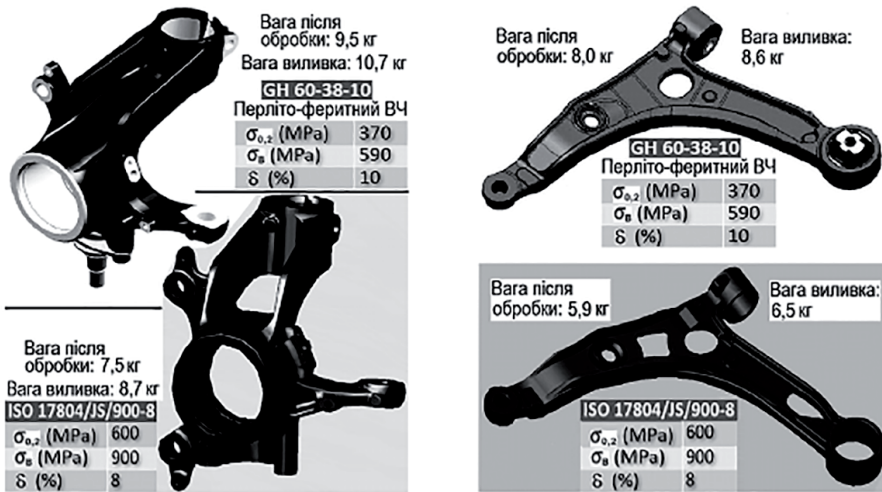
Деталі виливків рульового пристрою автомобіля з чавунів в литому стані (верхній ряд) і двофазного DP-ADI (нижній ряд) із зазначенням ваги і механічних властивостей [10, 13]
